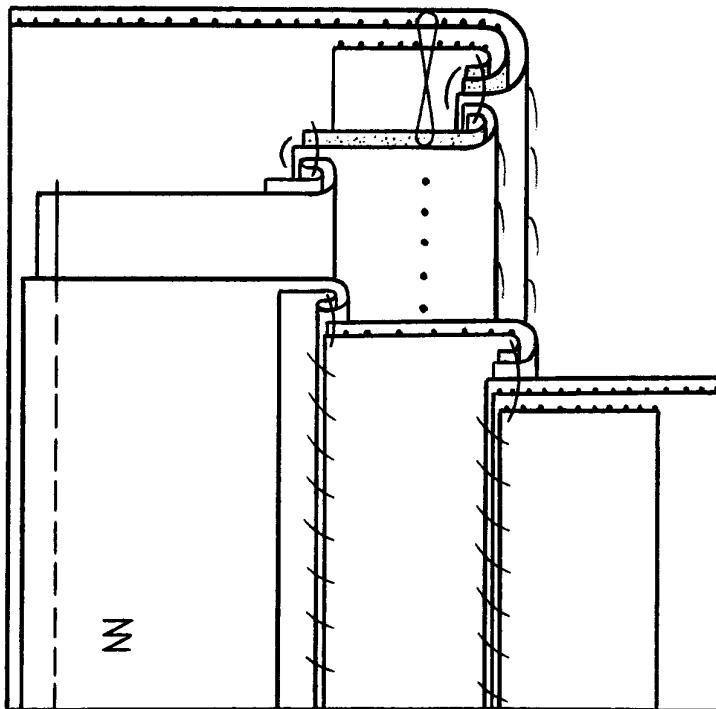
Сборочная схема прорезного кармана «в щель» с обтачкой и подзором из меха
